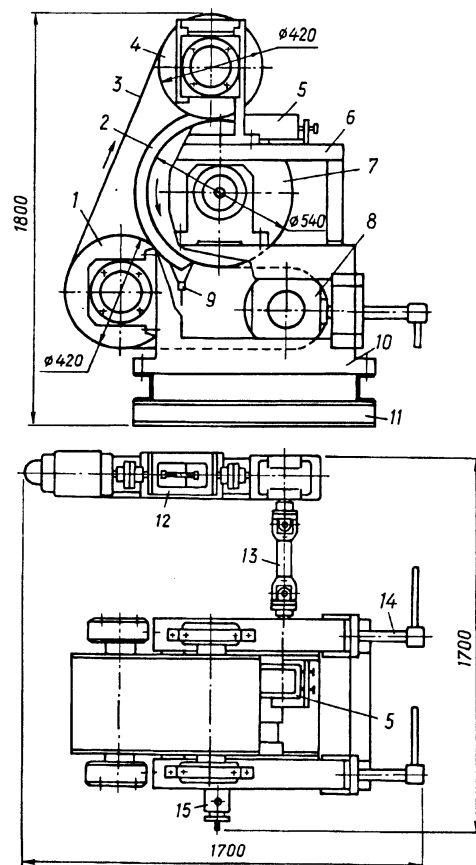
Конструкция экспериментальной установки: 1 — валок направляющий; 2 — охладитель ленты; 3 — рабочая лента; 4 — валок прижимной; 5 — коробка литниковая; 6 — стойка; 7 — колесо формообразующее; 8 — валок приводной; 9 — слив; 10 — клеть; 11 — рама; 12 — привод; 13 — вал карданный; 14 — винт; 15 — устройство для подачи воды в колесо
